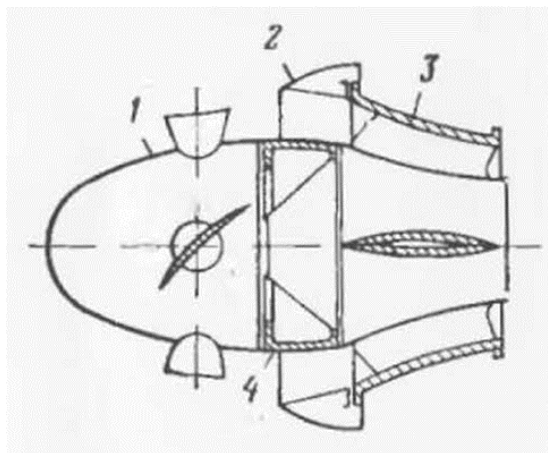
Вхідний пристрій ТГД: 1-обтічник втулки повітряного гвинта; 2 - зовнішнім обтічником; 3 - корпус вхідного пристрою; 4 - обтічник корпусу редуктора
